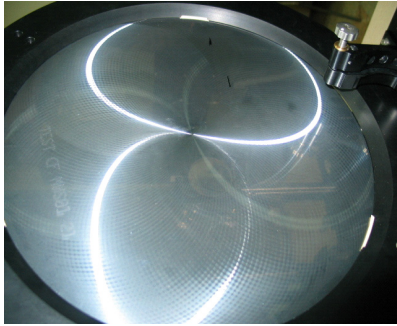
Tool mark가 있는 경우의 웨이퍼 사진
